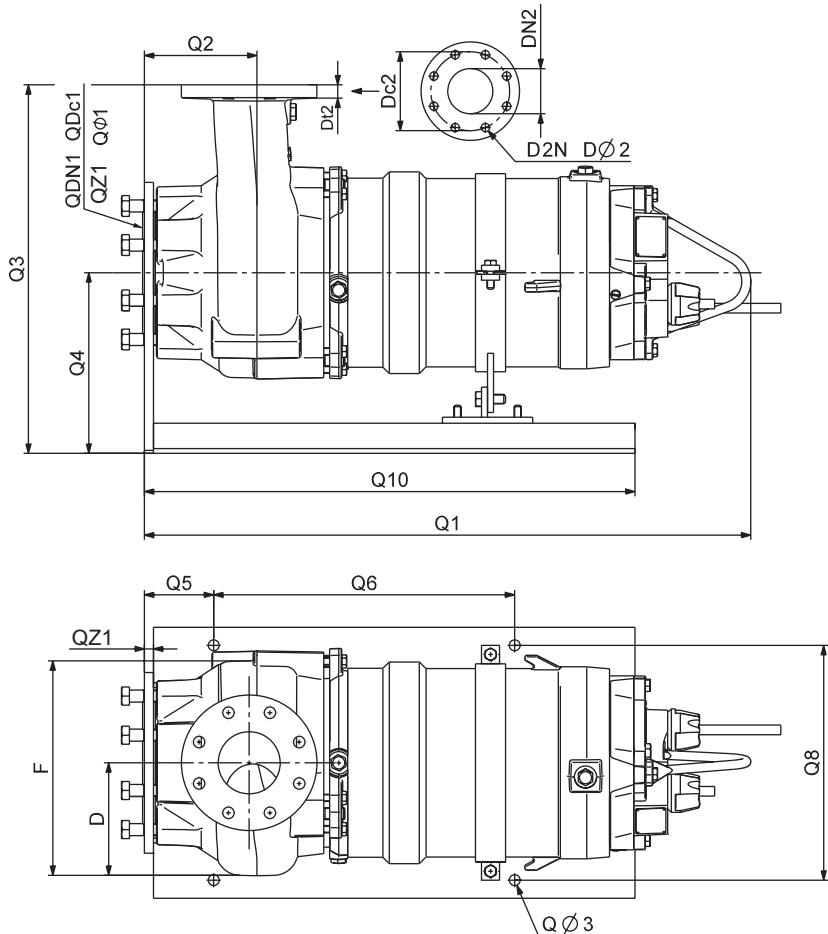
Габаритные размеры, сухая горизонтальная установка на опоре
